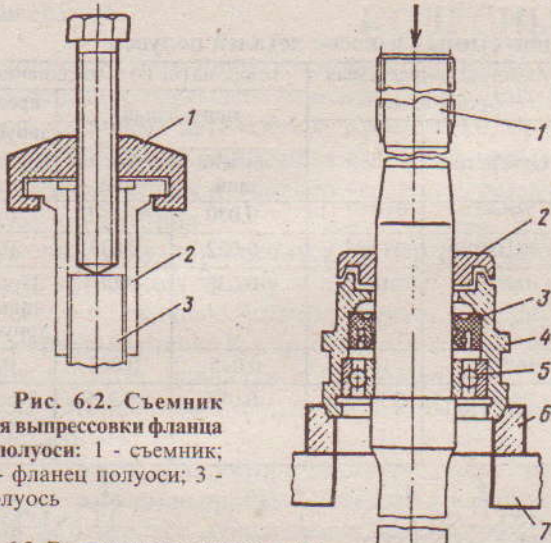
Съемник для выпрессовки фланца с полуоси: 1 - съемник; 2 - фланец полуоси; 3 - полуось
